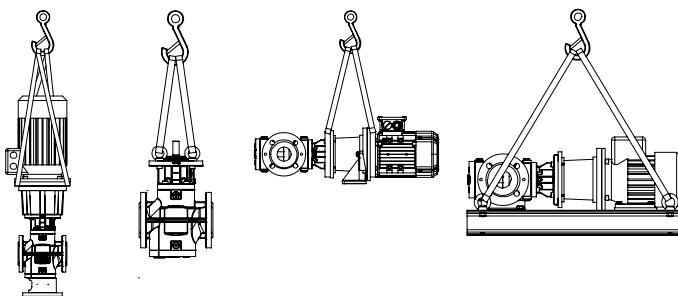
Befestigung Hebezeug - Prinzipbilder
